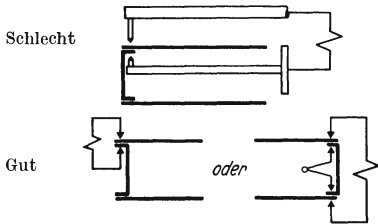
Schweißen eines Bodens im Hohlkörper. Abb. 40. Schweißen von Werkstücken mit sperriger Gestalt. Abb. 39 u. 40. Sperrige Gestalt des Werkstückes erzwingt mit großer Armausladung und -öffnung teure Maschinen mit schlechtem Wirkungsgrad und Leistungsfaktor. Abhilfe durch Änderung der Gestalt oder des Stromweges.
